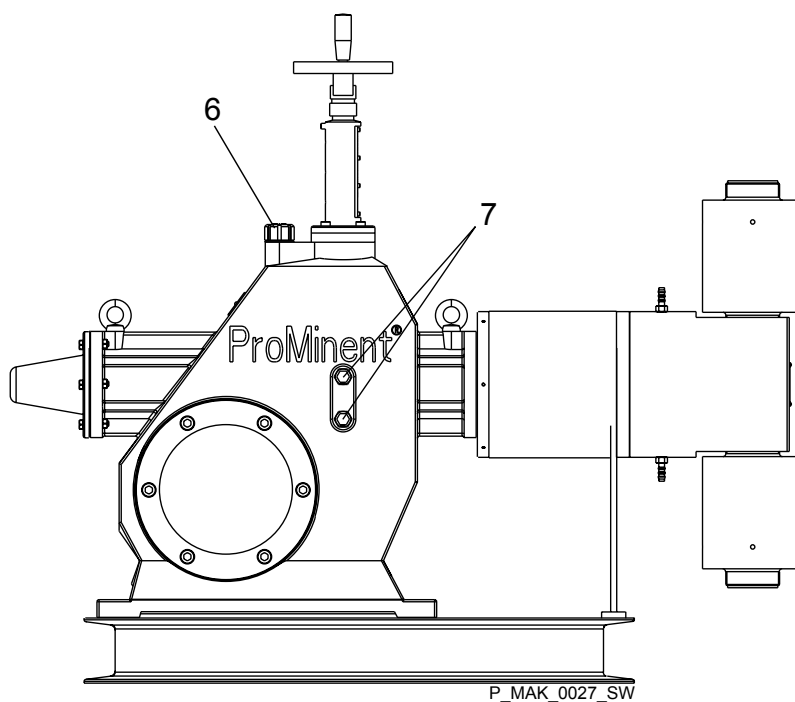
Vista del lado opuesto al motor (aquí M5Ka H)
